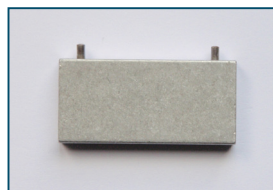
Wechselwerkzeug für Anschlussadapter
